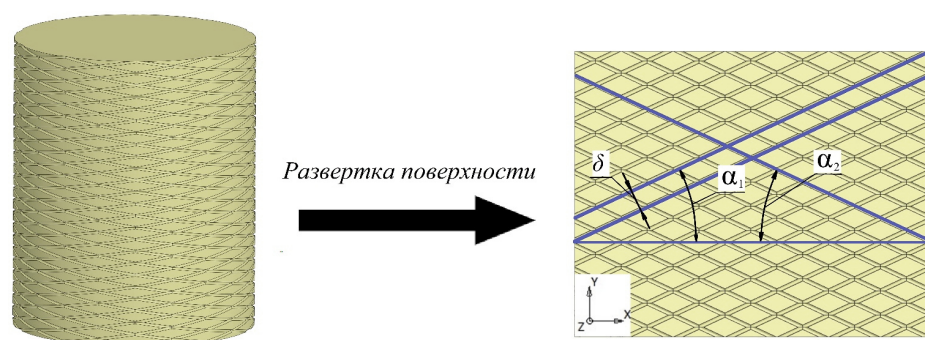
Развертка поверхности цилиндра (титановой заглушки) с канавками от лазерной обработки на плоскость
